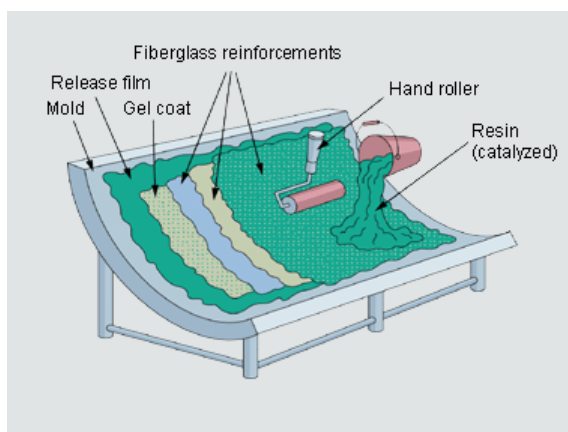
Rappresentazione schematica del processo di hand lay-up. In figura gli elementi principali: lo stampo (mold), la pellicola di distaccante (release film), il rivestimento di gel (gel coat), rinforzi di fibra di vetro, rullo (hand roller) e resina premiscelata con il catalizzatore (resin catalyzed).
